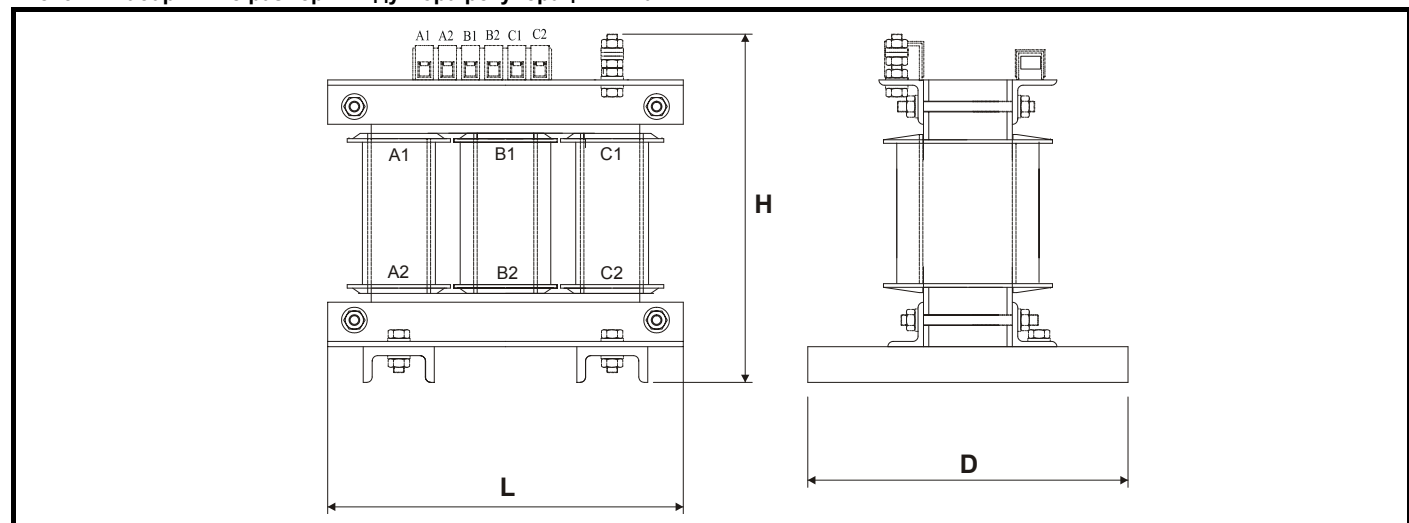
Габаритные размеры индуктора рекуперации типа 2
